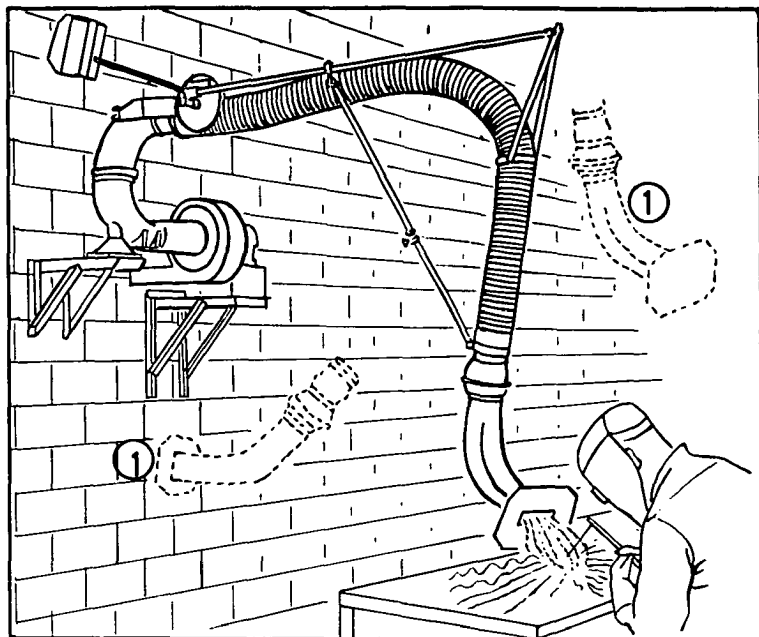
Aspiration des fumées produites par le soudage électrique au moyen d'une bouche d'aspiration mobile.
